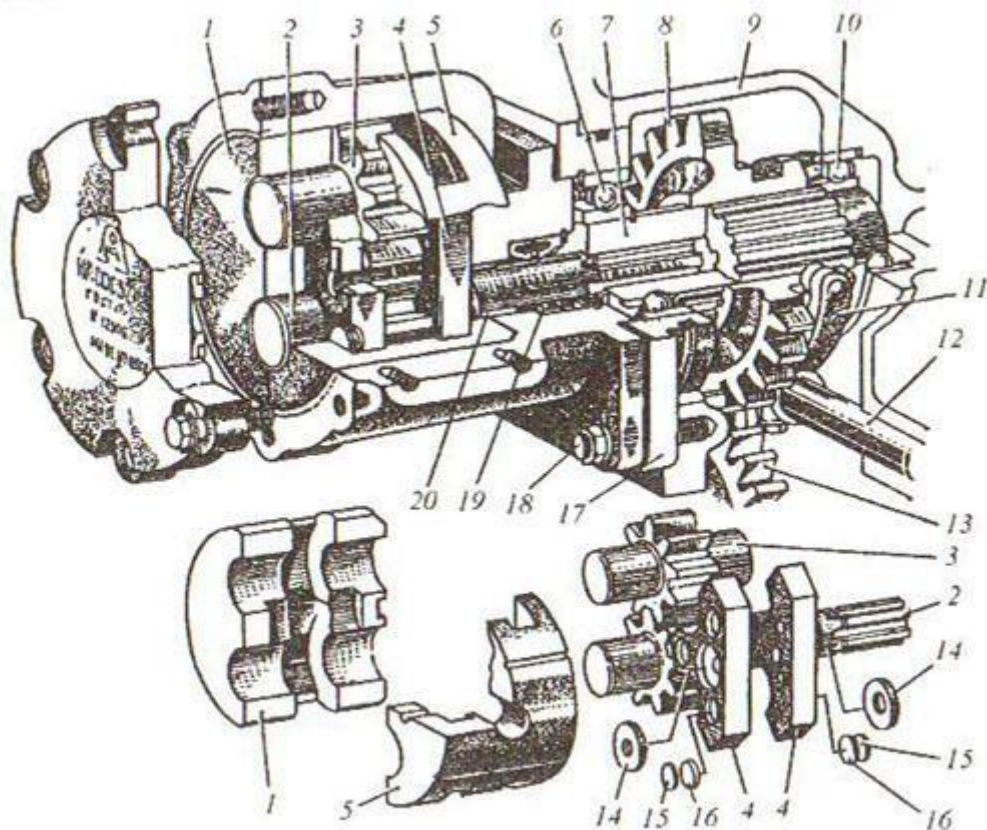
Масляный насос НШ-32-3: 1 - подшипниковая обойма; 2 - ведущая шестерня; 3 - ведомая шестерня; 4 - пластик; 5 - поджимная обойма; 6,10 - шарикоподшипники; 7 - вал; 8 - шестерня; 9 - корпус; 11 - вилка; 12 - валик управления; 13 - промежуточная шестерня; 14 - манжета; 15 - шайба; 16 - манжета; 17 - стакан подшипника; 18 - шпилька; 19 - манжета; 20 - втулка центрирующая
